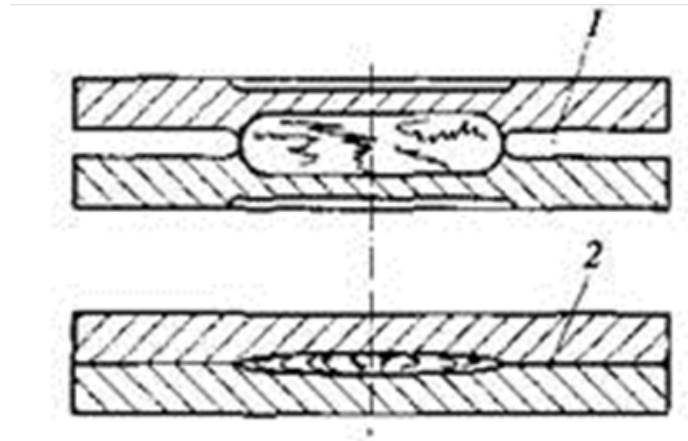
Схема формування проміжку між деталями і розміру ядра точки від ступеню деформації при класичному (1) і прецизійному (2) контактному зварюванні
